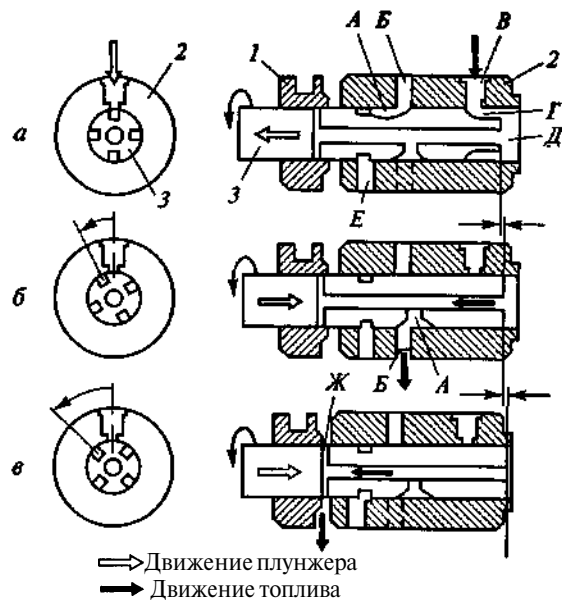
Схема работы распределительного одноплунжерного насоса: а — наполнение; б — активный ход; в — отсечка; 1 — дозатор, 2 — корпус, 3 — плунжер; А — распределительный паз; Б — нагнетательный канал; В — впускное окно; Г — выточка; Д — надплунжерная полость; Е — окно; Ж — радиальный канал
